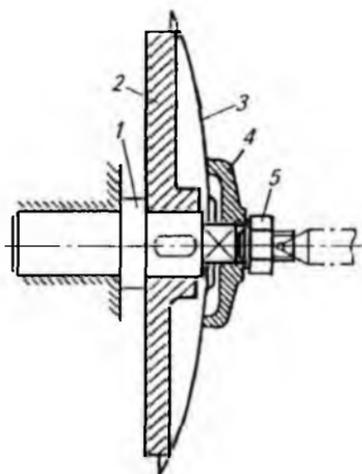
Схема установки диска на токарном станке для заточки лезвий
